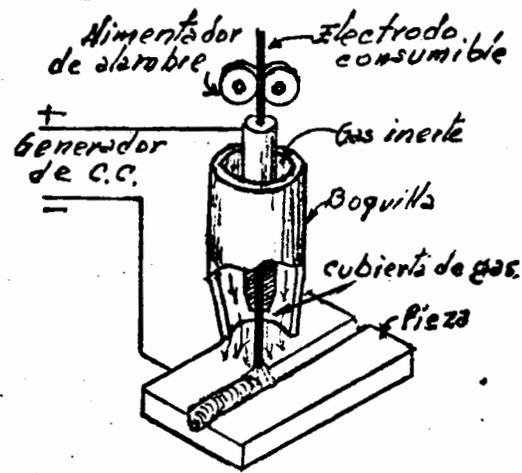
SOLDADURA DE ARCO CON ELECTRODO METALICO Y GAS INERTE. (MIG)
